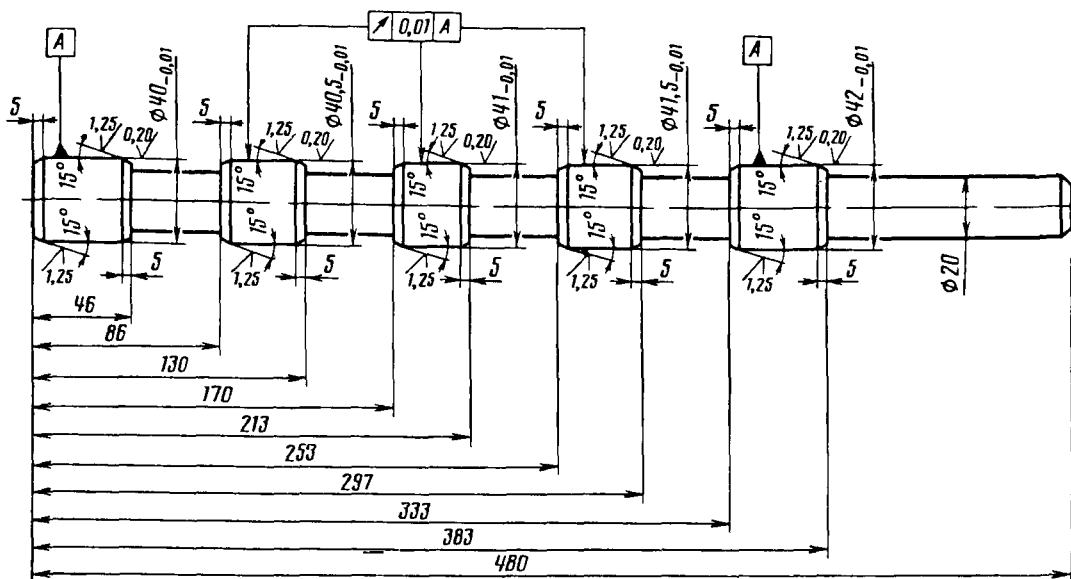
Оправка для проверки соосности подшипников распределительного вала
